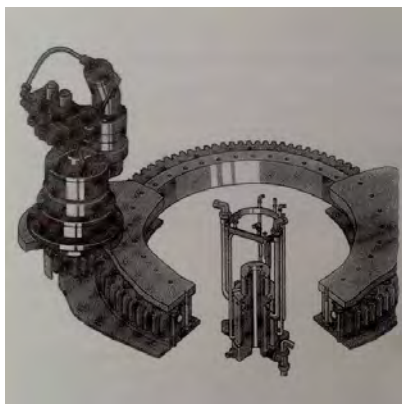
Гидравлический привод поворотного механизма с планетарным приводом и однорядным шариковым поворотным соединением. Ротор для гидравлического и пневматического управления. Корпус контактного кольца для электрического управления, смонтированный на роторе, электропроводка проходит через отверстие в роторе. Электрическая часть здесь не представлена
